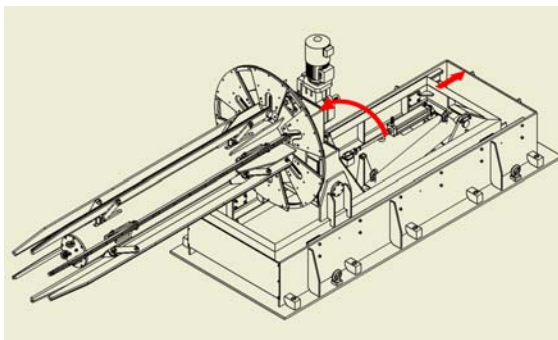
Aufnahmedorn parallel zur Drahtablaufaufrichtung
